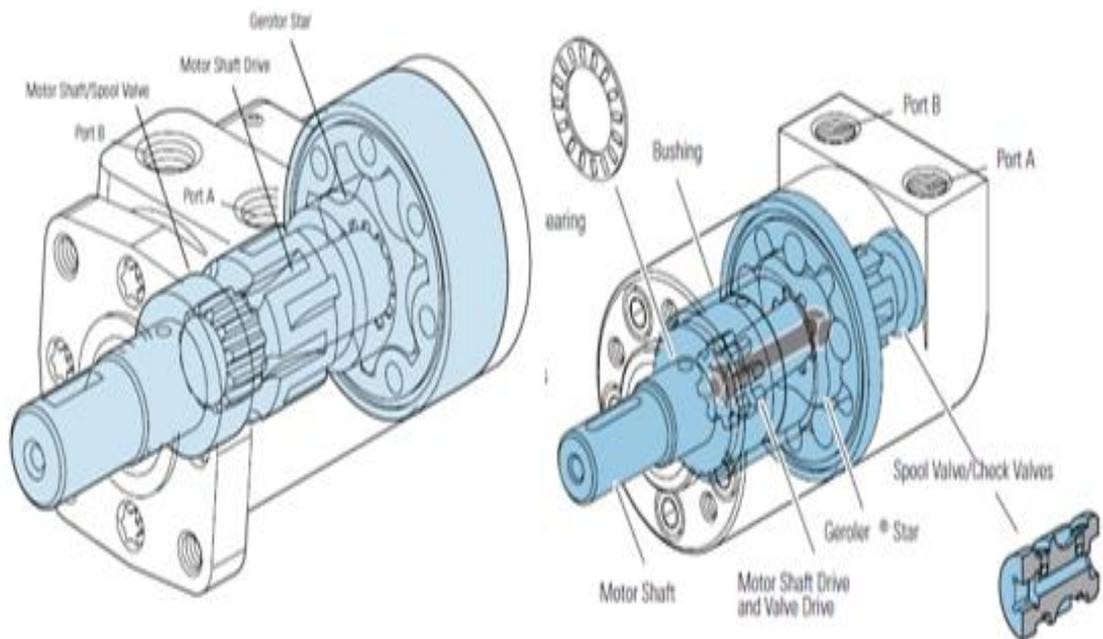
Construcción de motores tipo orbital con válvulas de carrete.[20]
